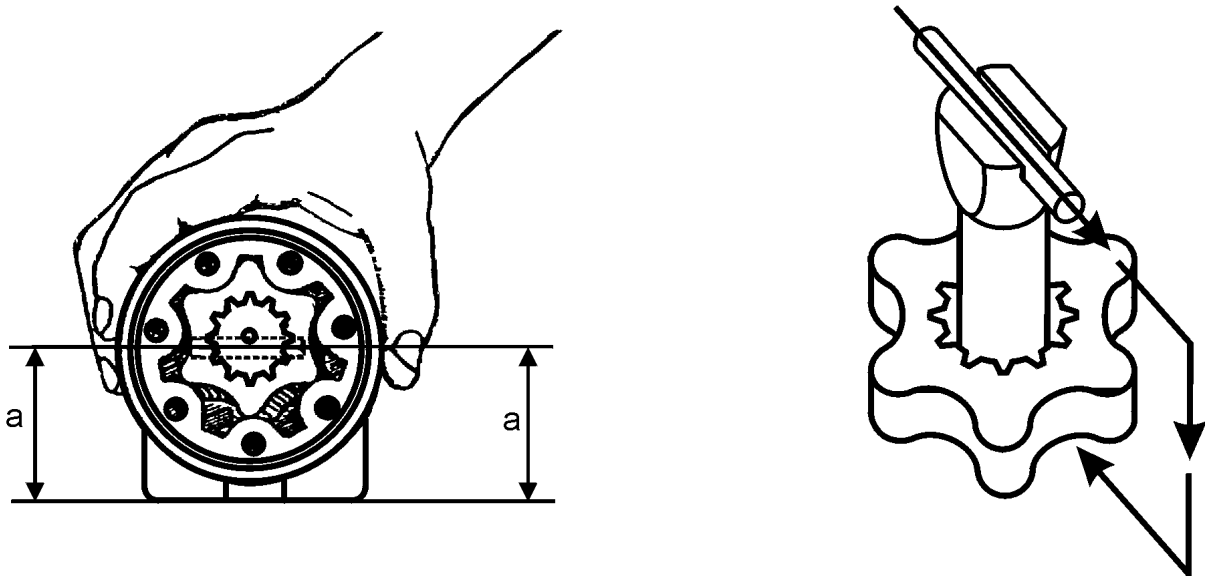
В.7G. Взаимное расположение валика кардана, ротора и корпуса ротора при сборе
